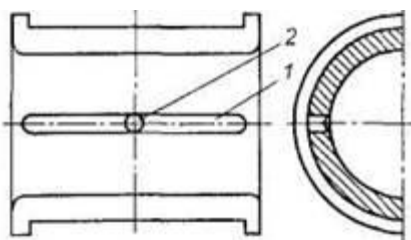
Вкладыш: 1 — канавка; 2 — отверстие для подвода смазки
